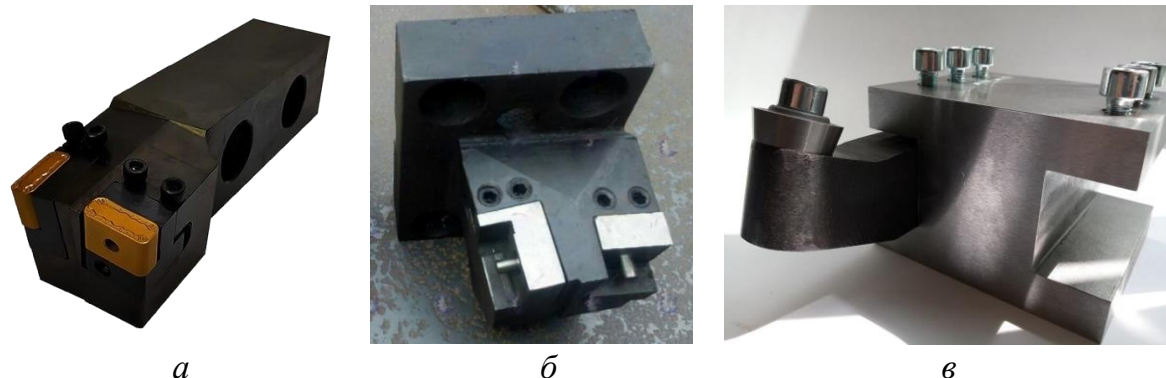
Различные конструкции резцов с СМП для обработки бандажей колесных пар: *a* – резец с тангенциальным креплением СМП; *б* – резцовая головка с тангенциальным креплением СМП; *в* – резец с радиальным креплением СМП
